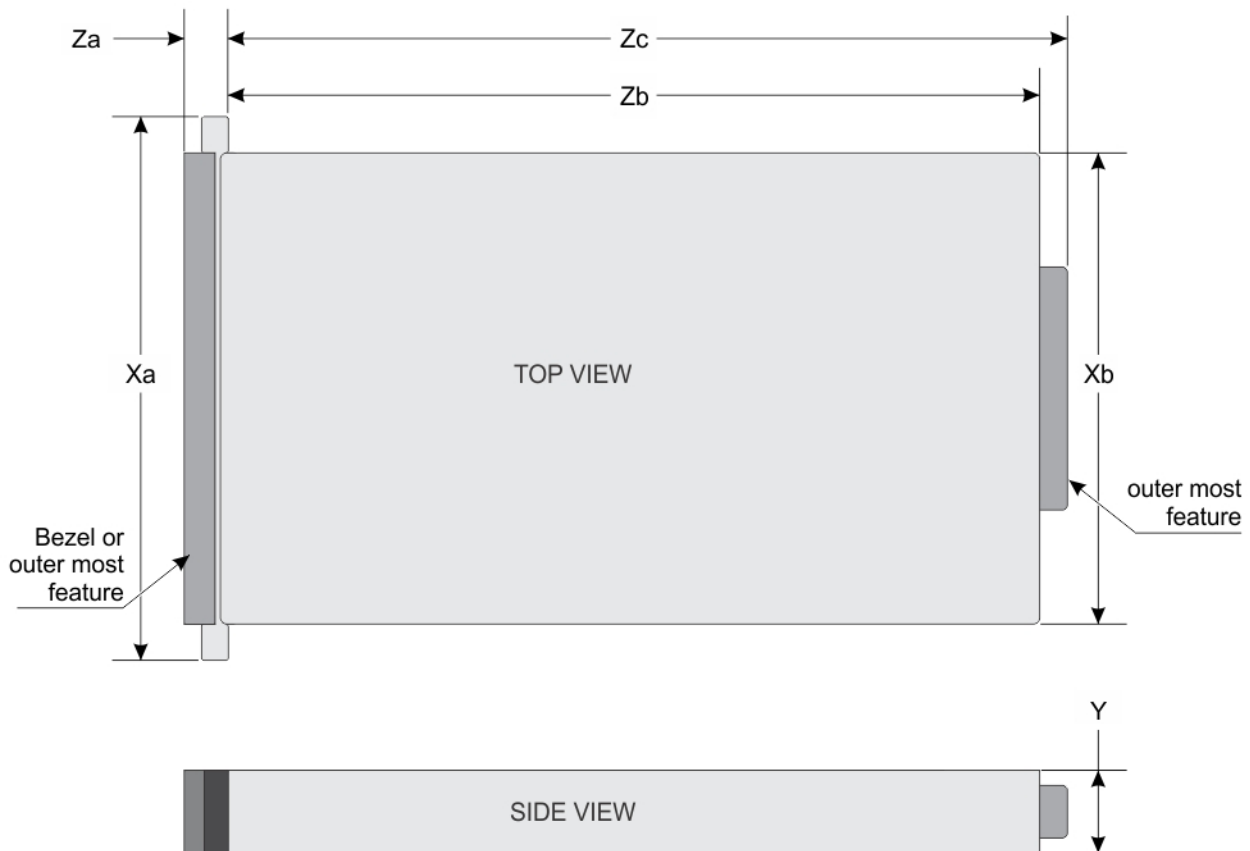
Die Gehäuseabmessungen des PowerEdge C6320-Systems
